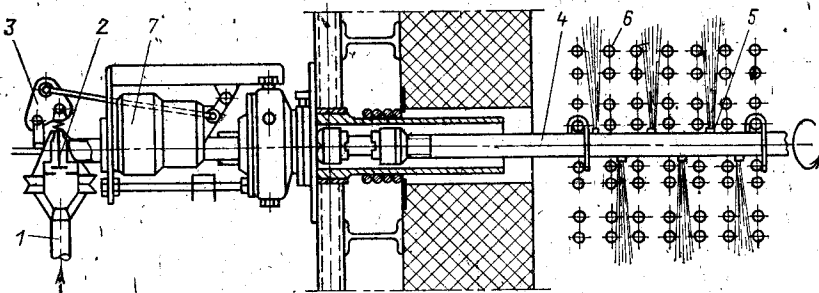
Паровой обдувочный прибор ОПК-7 конвективного перегревателя: 1 — подача пара; 2 — клапан; 3 — механизм управления клапаном; 4 — обдувочная труба из жаропрочной стали; 5 — сопло; 6 — трубка перегревателя; 7 — электрический двигатель
